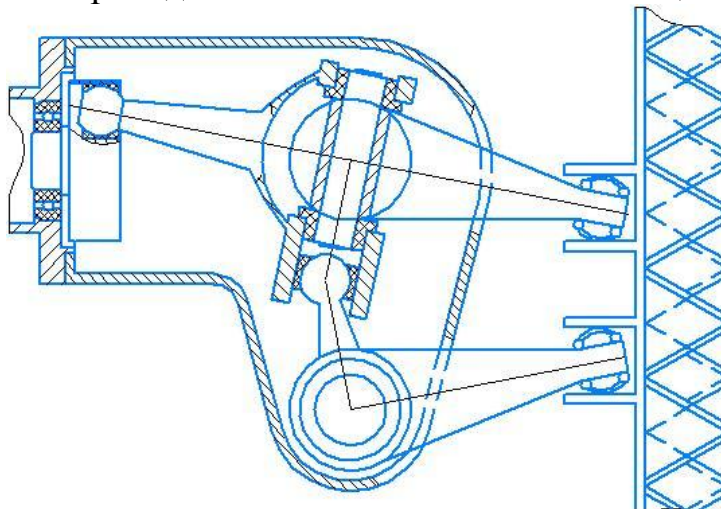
Привод ножей механизмом «Качающаяся вилка»
